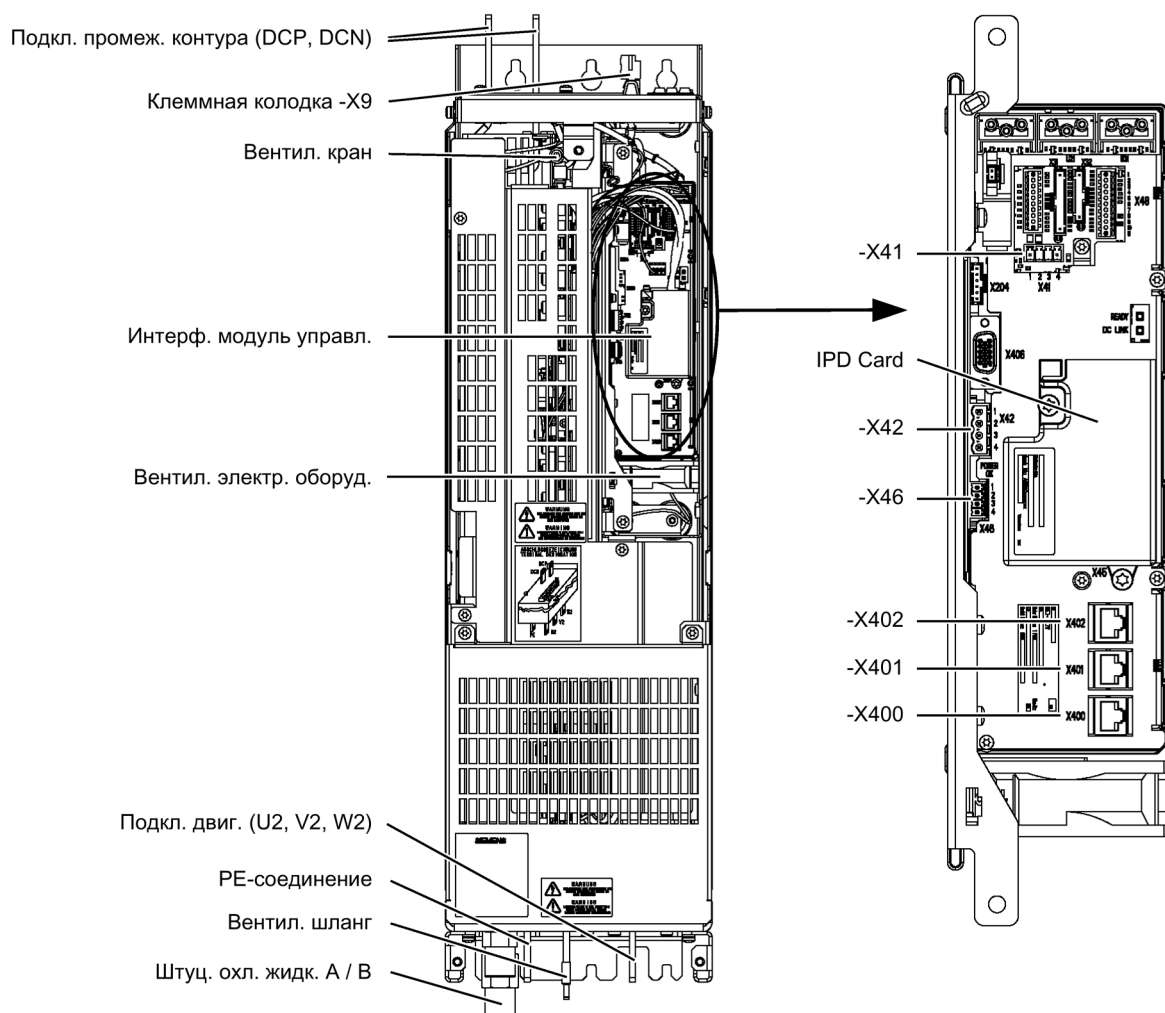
Модуль двигателя, типоразмер HXL
